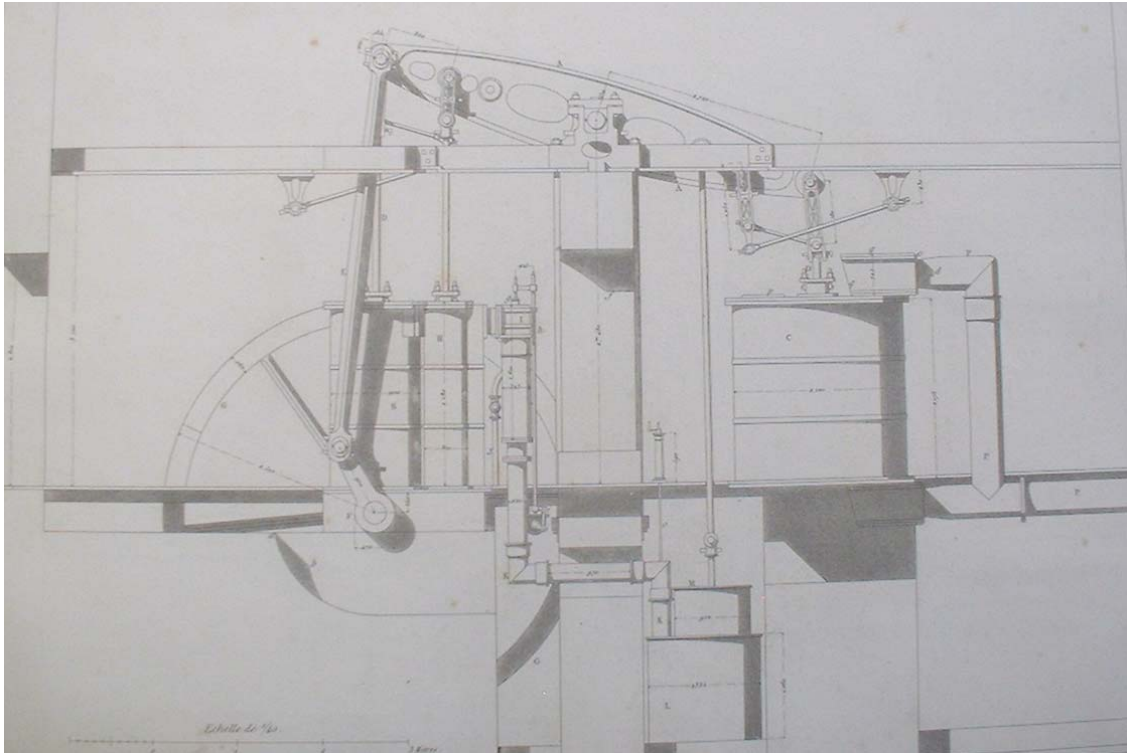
, Pl 59, machine soufflante, Leblanc, 40x22 cm.
